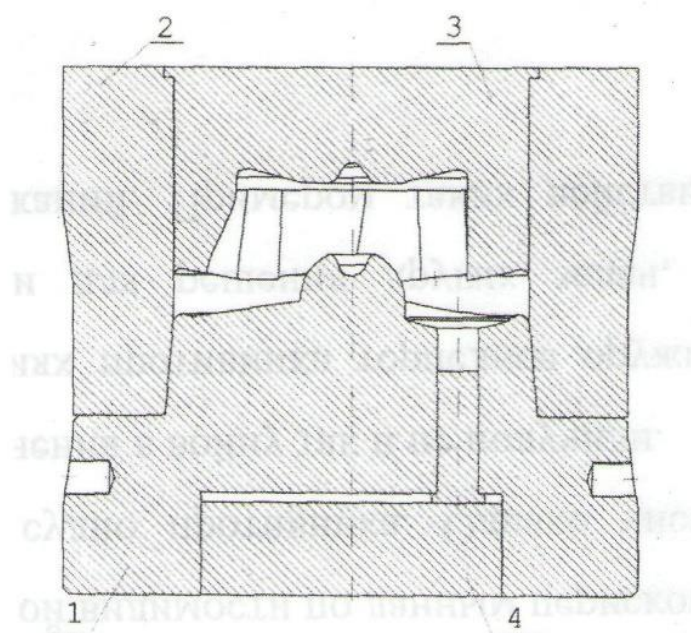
Схема штампа для об'ємного штампування заготовки сталевого соплового блоку фурми: 1 – матриця; 2 – обойма; 3 – пуансон; 4 – виштовхувач
